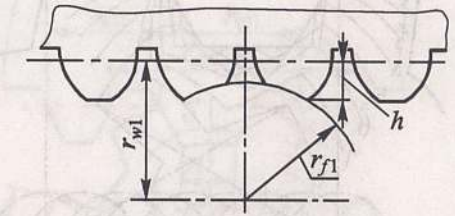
Профиль червячной фрезы с корригированной линией выступов зубьев
